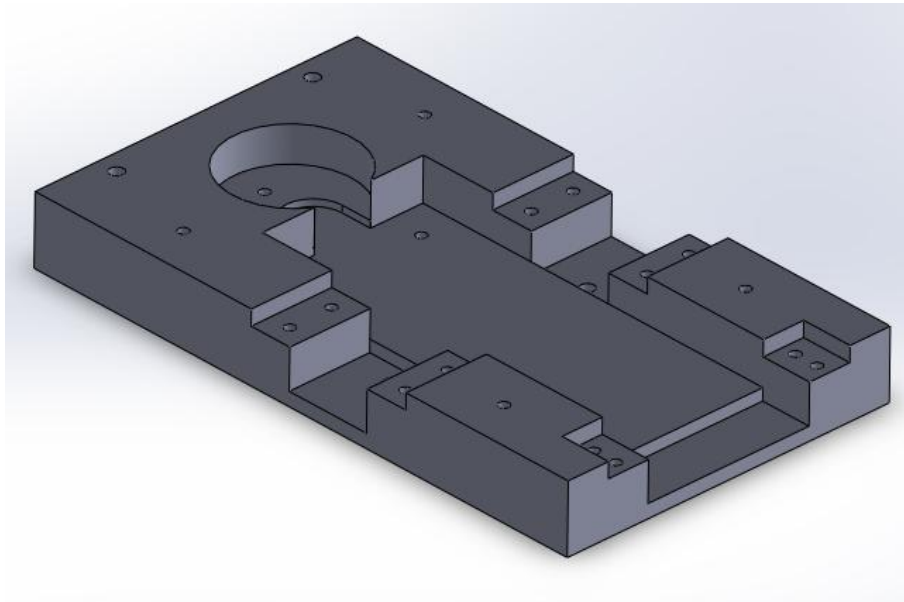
Vista 3D de la pieza (parte móvil del molde) diseñada en SolidWorks.
